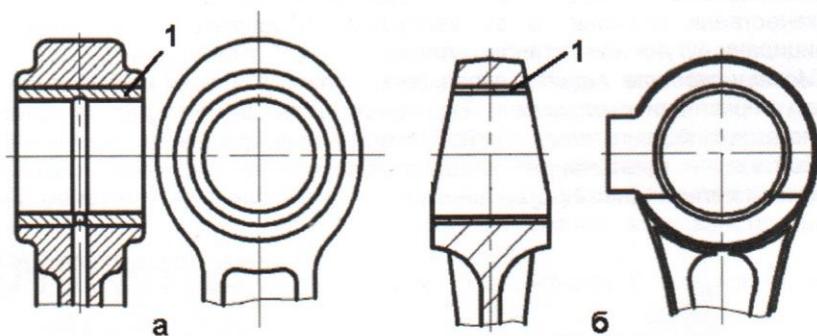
Мотовилки за едноредови и V-образни двигатели: а-за едноредов двигател с двойно I-образно сечение, с канал за смазване и с перпендикулярно поставена долната глава; б-за V-образен двигател с двойно I-образно сечение; 1-глава; 2-стъбло; 3-долна глава; 4-канал за масло.
